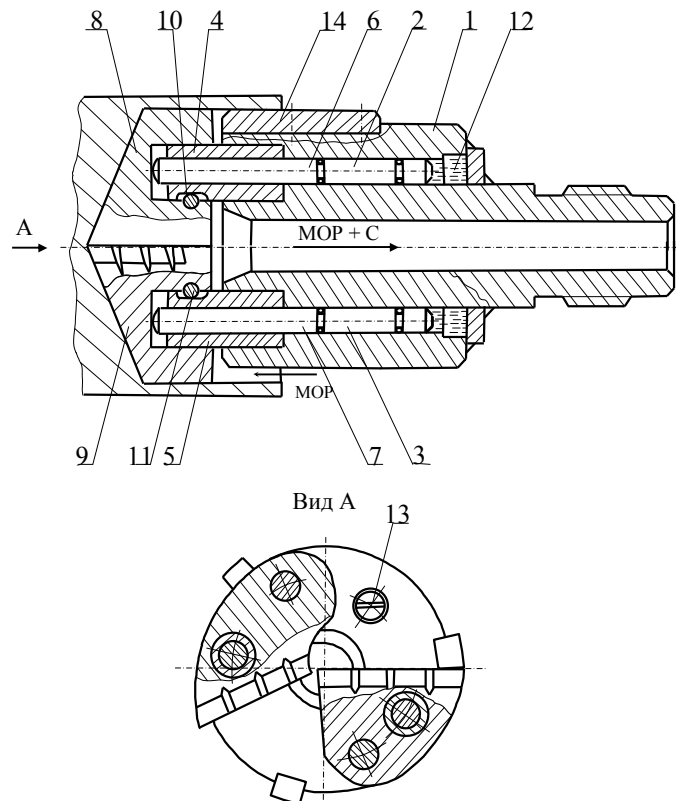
Конструкція збірного свердла з гідравлічним міжлезовим зв'язком
